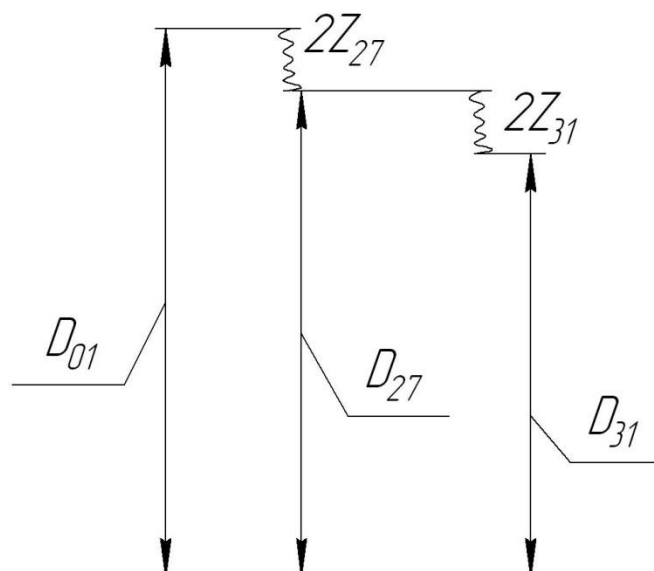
Размерная схема обработки поверхности $\varnothing 124_{-0,063}$
